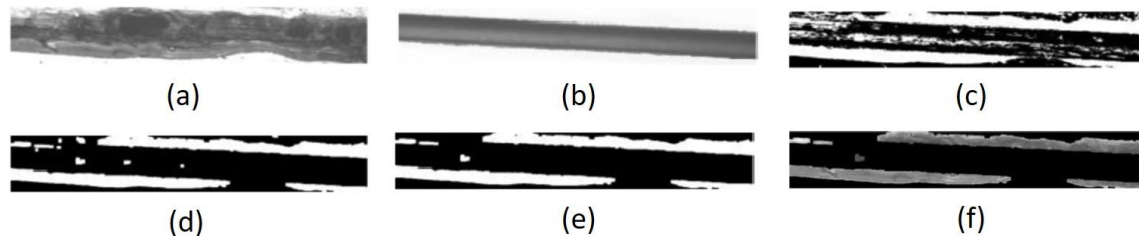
Extracción de los elementos característicos de la soldadura (Fuente: [28])
